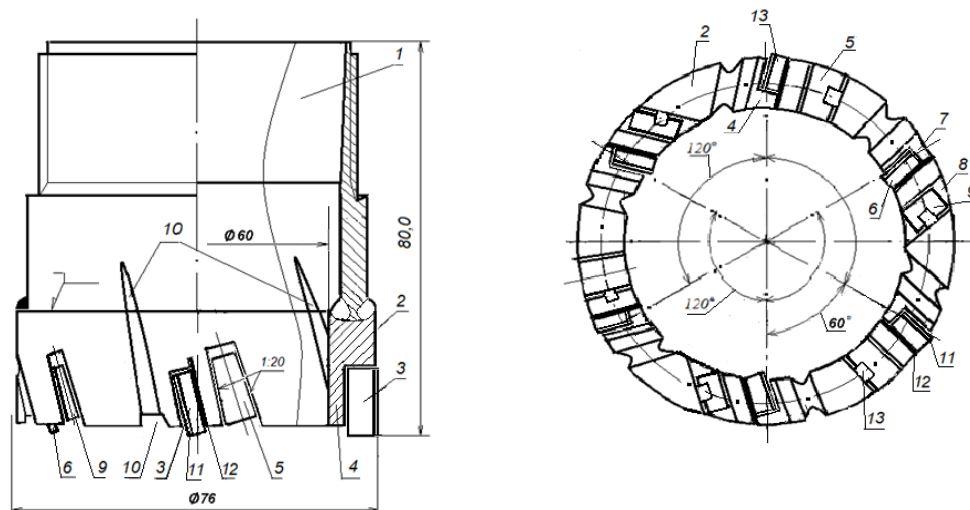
Буровая коронка с пайкоклинным способом крепления резцов: 1 – корпус коронки; 2 – корончатое кольцо; 3 – пластины-резцы скважинообразующие; 4 – стенка паза внутренняя; 5 – клин; 6 – пластины-резцы кернообразующие; 7 – стенка паза наружная; 8 – паз под клин; 9 – клин; 10 – каналы и пазы промывочные; 11 – слой резца режущий; 12 – припой трехслойный марки ТП-1М; 13 – стопор клина.
